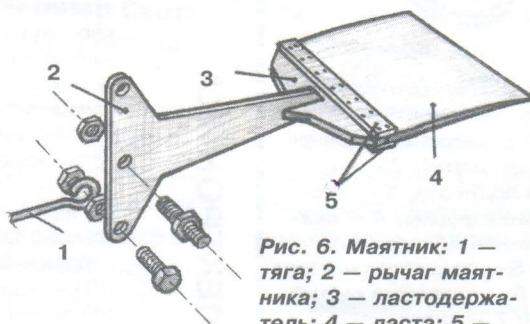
Маятник: 1 — тяга; 2 — рычаг маятника; 3 — ластодержатель; 4 — ласта; 5 — крепежные пластины.
